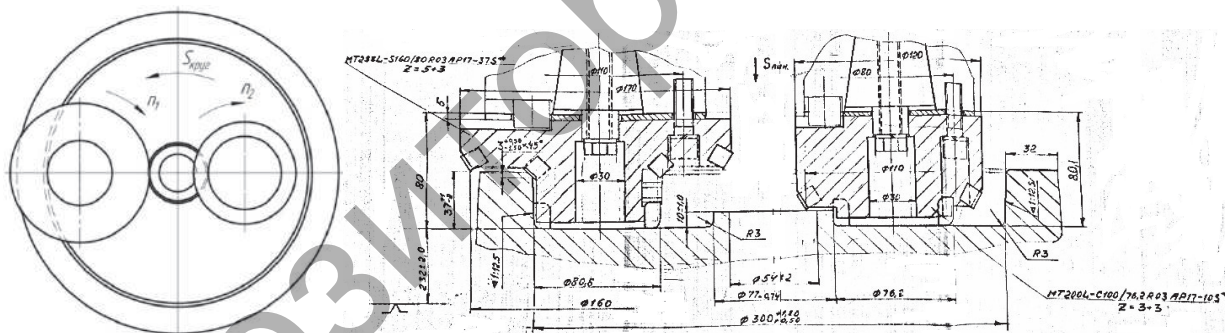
Эскиз детали, подлежащей обработке круговым фрезерованием
